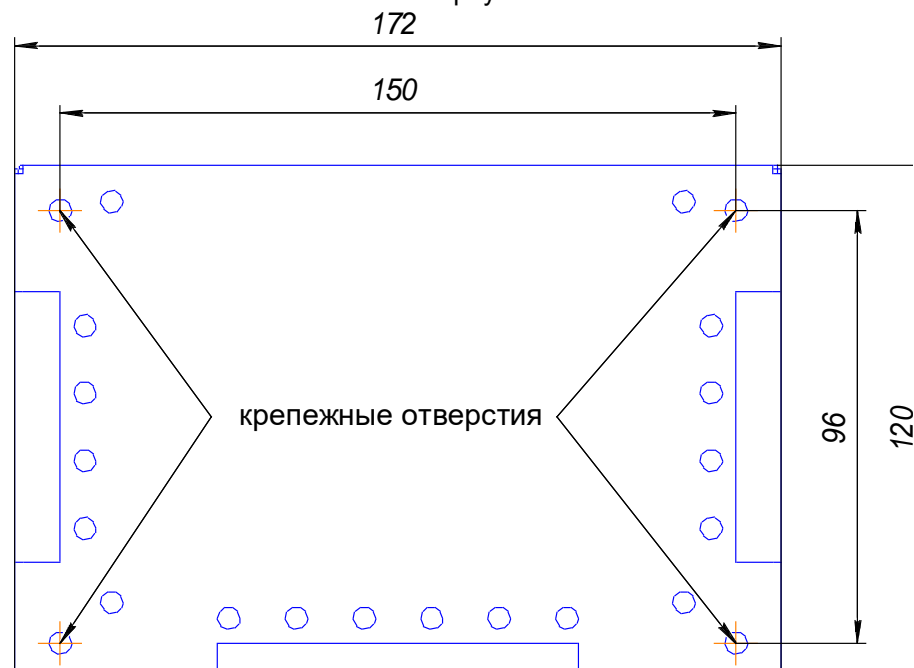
б. Разметка крепления АКШ ФИДШ.426461.001-01 в металлическом корпусе
